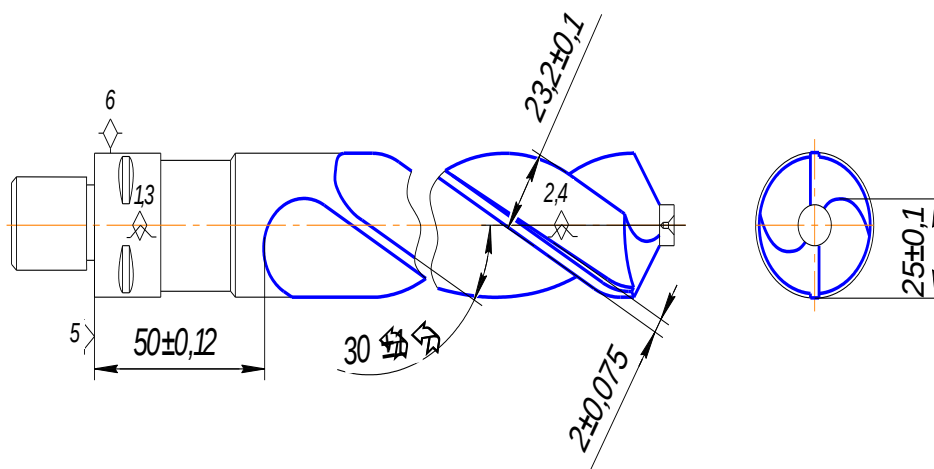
Операционный эскиз на фрезерование стружечной канавки
